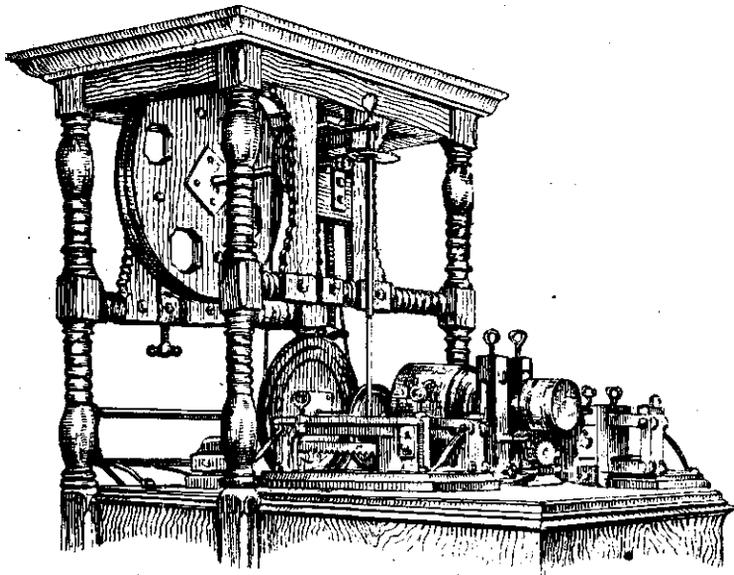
Токарно-копировальный станок 1712 г. (вид спереди на механизмы привода и подачи супорта).
